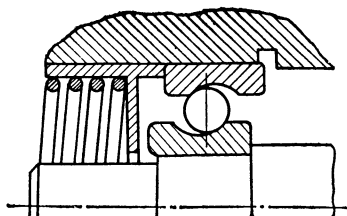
Подшипниковый узел с предварительным осевым натягом
